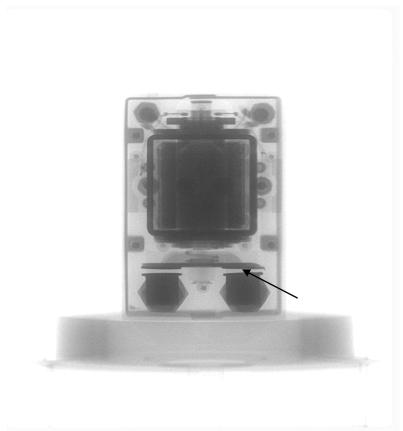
particolare del contatto A1 non parallelo alla parte fissa.
